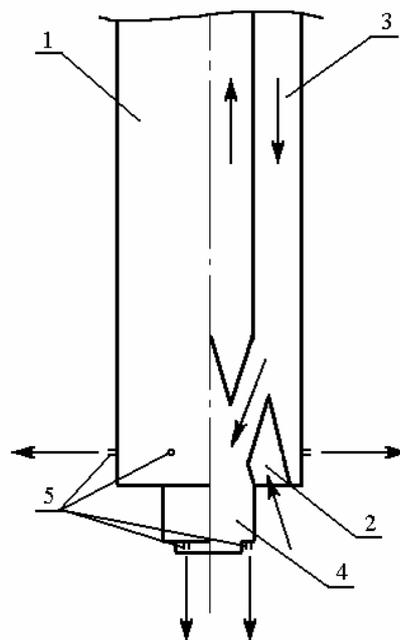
Схема ґрунтозаборного пристрою: 1 – корпус; 2 – всасуючий патрубок; 3 – напорна поллю; 4 – головка; 5 – розмиваючі форсунки
